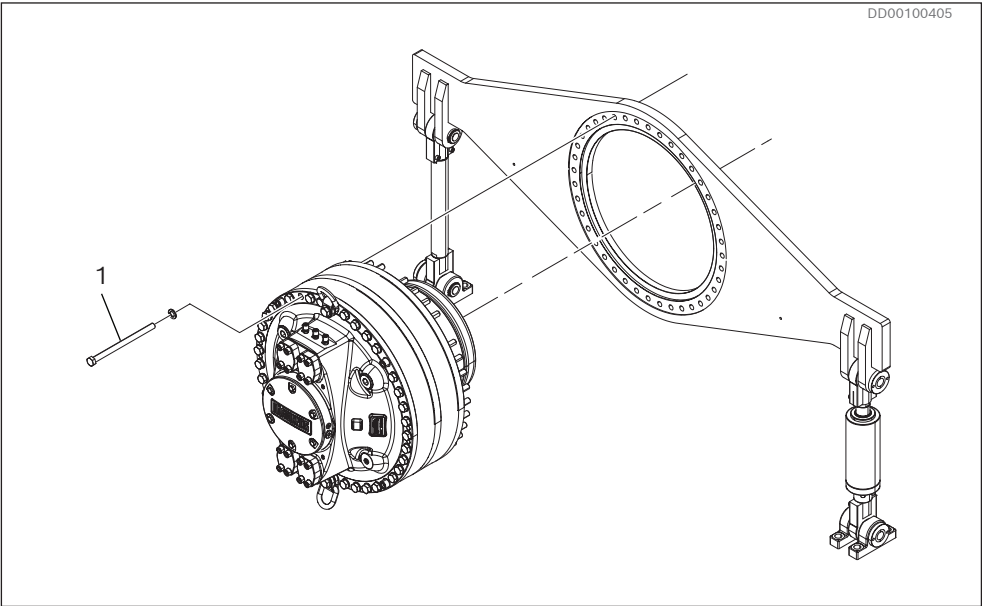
Montage von doppelseitiger Drehmomentstütze DTCB 0400 bis DTCB 1120 für CB 280 bis CB 1120
